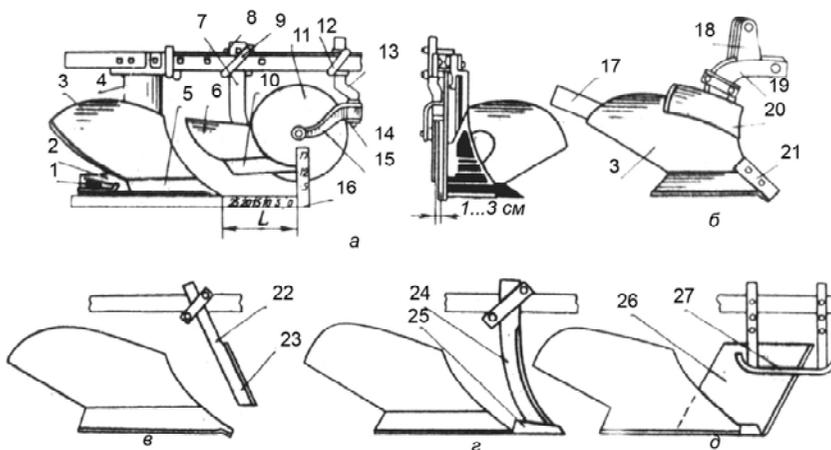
Установка предплужника и дискового ножа (а), углоснима (б), черенкового (в и з) и плоского (д) ножей:
